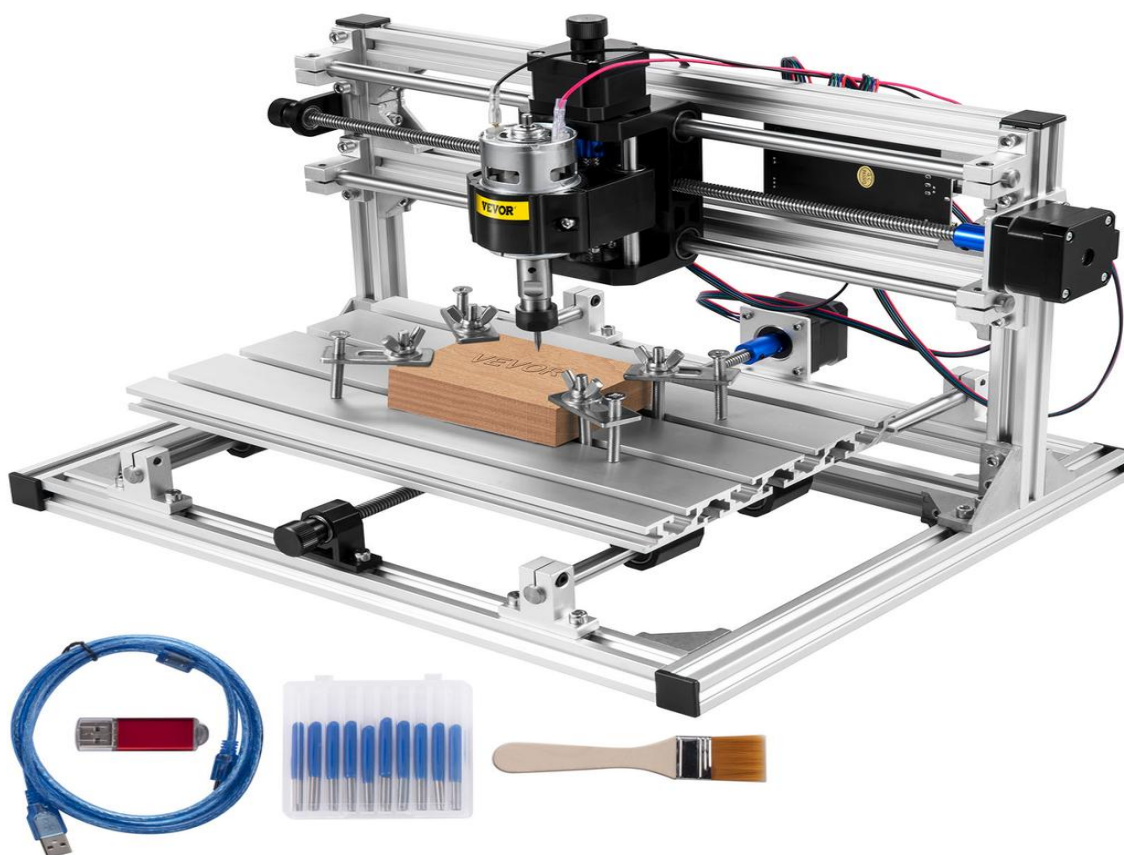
Побутовий фрезерний верстат з ЧПК.
